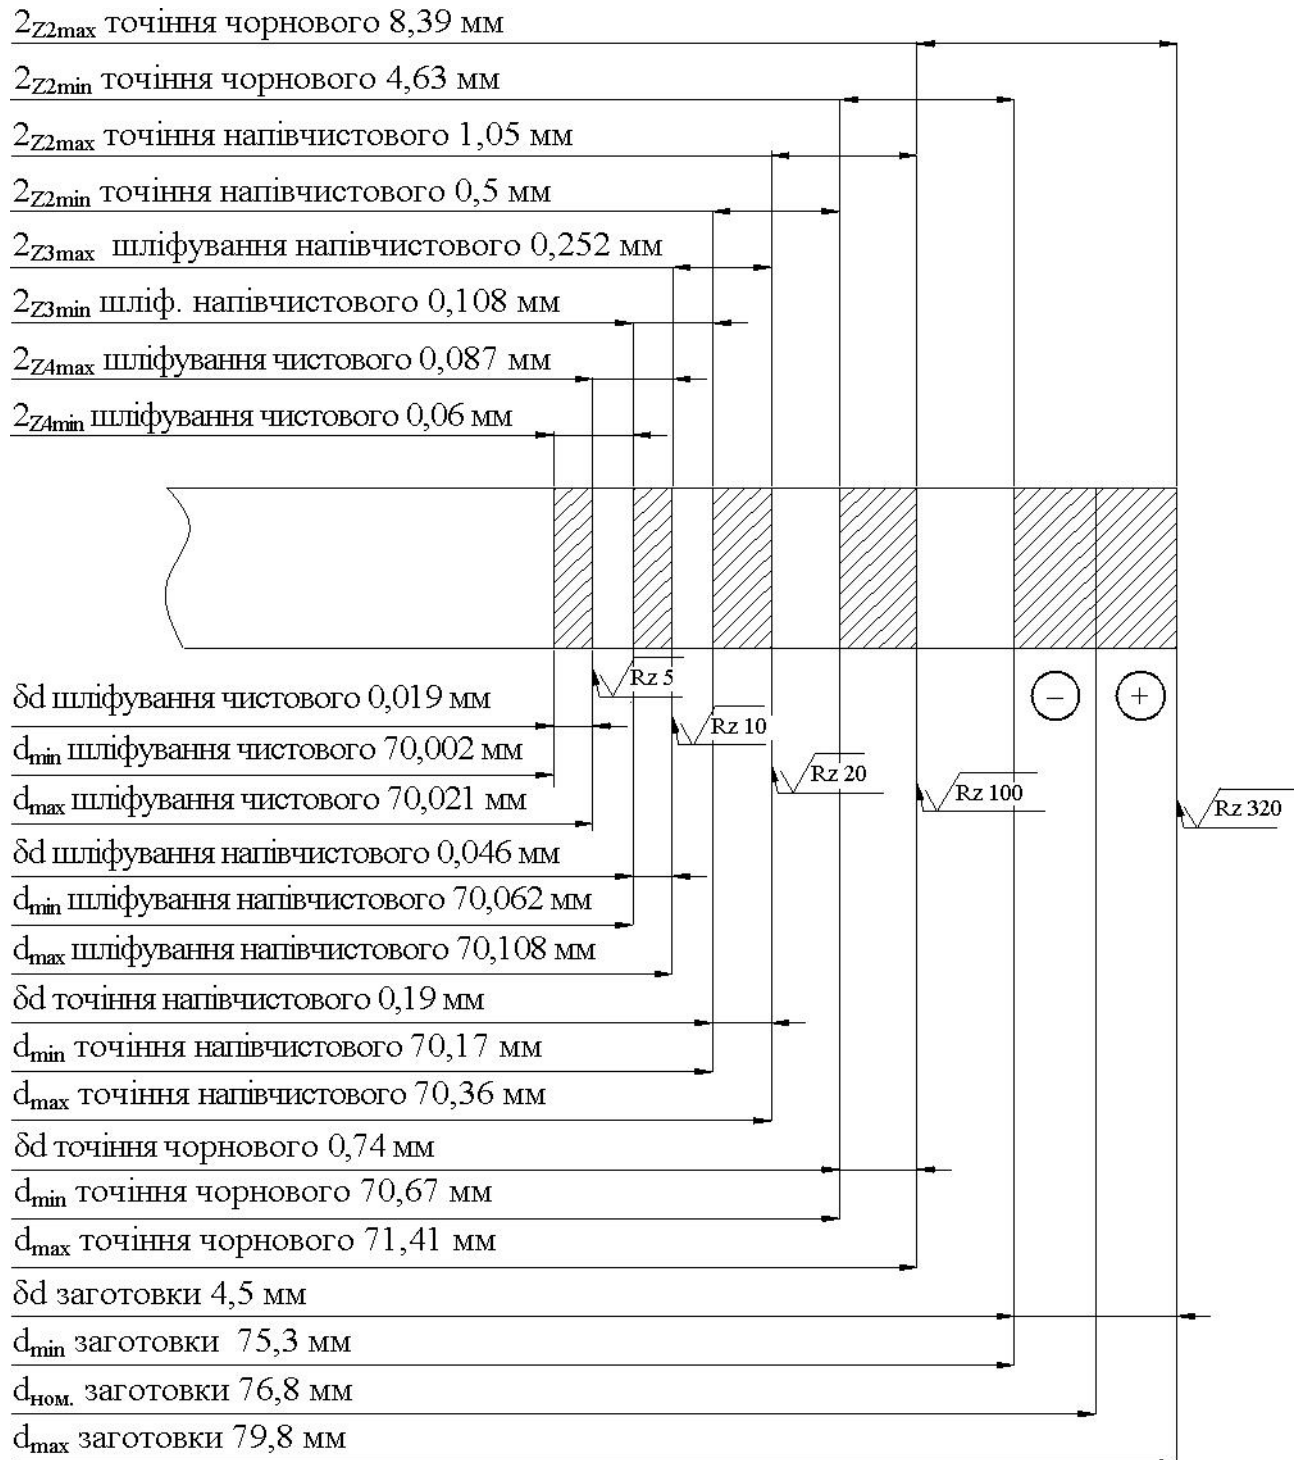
Схема розташування припусків для одержання поверхні  $\varnothing 70k6$  деталі «Вал» 09.412
